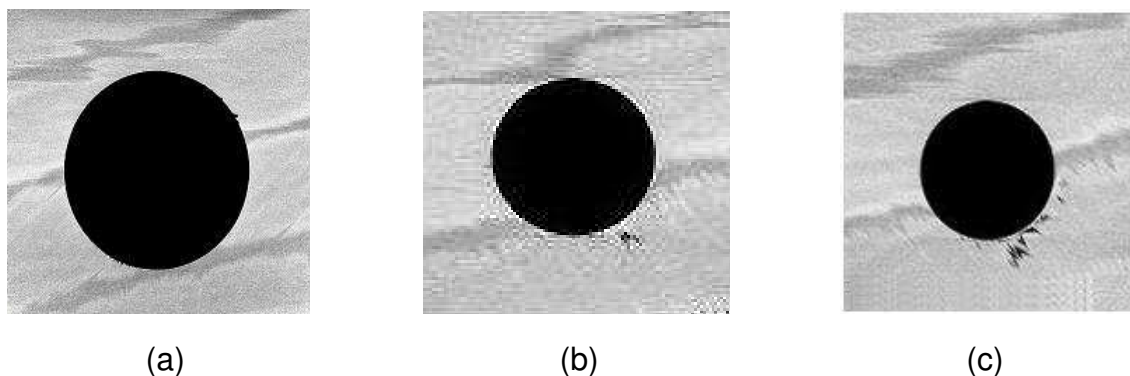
CT- Aufnahmen einer Senkkopfbohrung (a) gleich nach Bohrereintritt, (b) ca. in der Mitte der Probe und (c) unmittelbar vor Austritt des Bohrers (frontale Ansicht).
